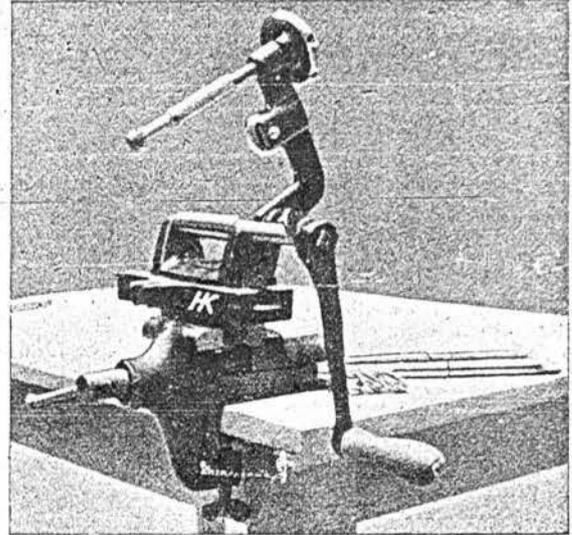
Die Maschine mit hochgehobener Schraubspindel zum Auswechseln der Profillrollen.
